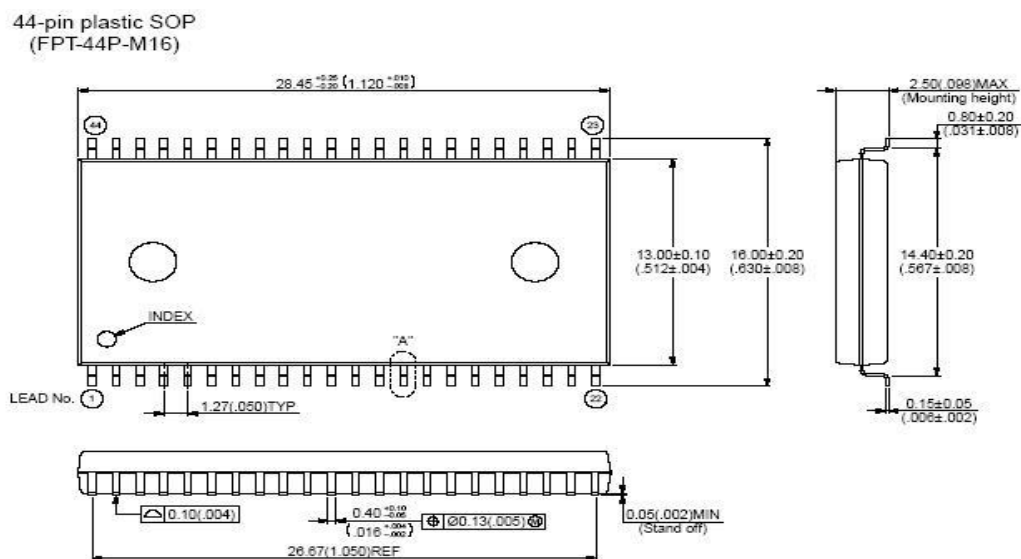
Конструктивні розміри корпусу мікросхеми FM21L16-60-TG
